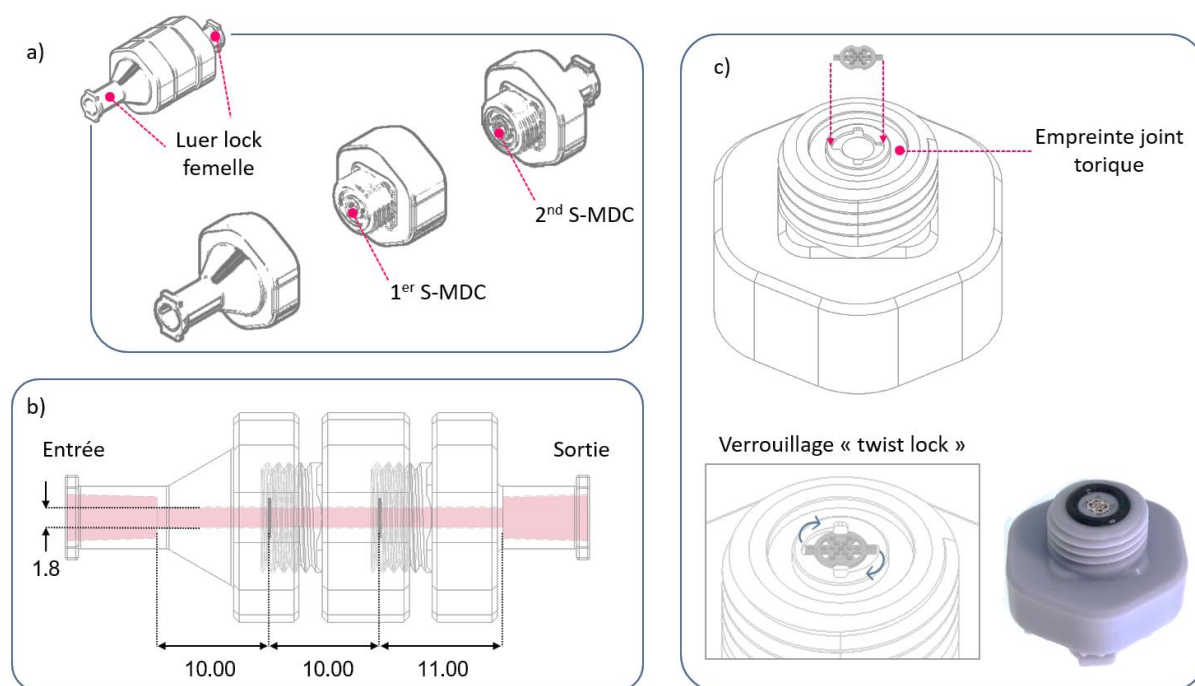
Principe et dimensions du holder. a) Exemple de holder accueillant deux S-MDCs positionnés en série. b) Vue de coupe d'un holder accueillant deux S-MDCs positionnés en série et dimensions typiques du canal. Les dimensions sont exprimées en mm. c) Empreinte permettant de positionner le S-MDC et de le verrouiller selon le principe « twist lock ».
